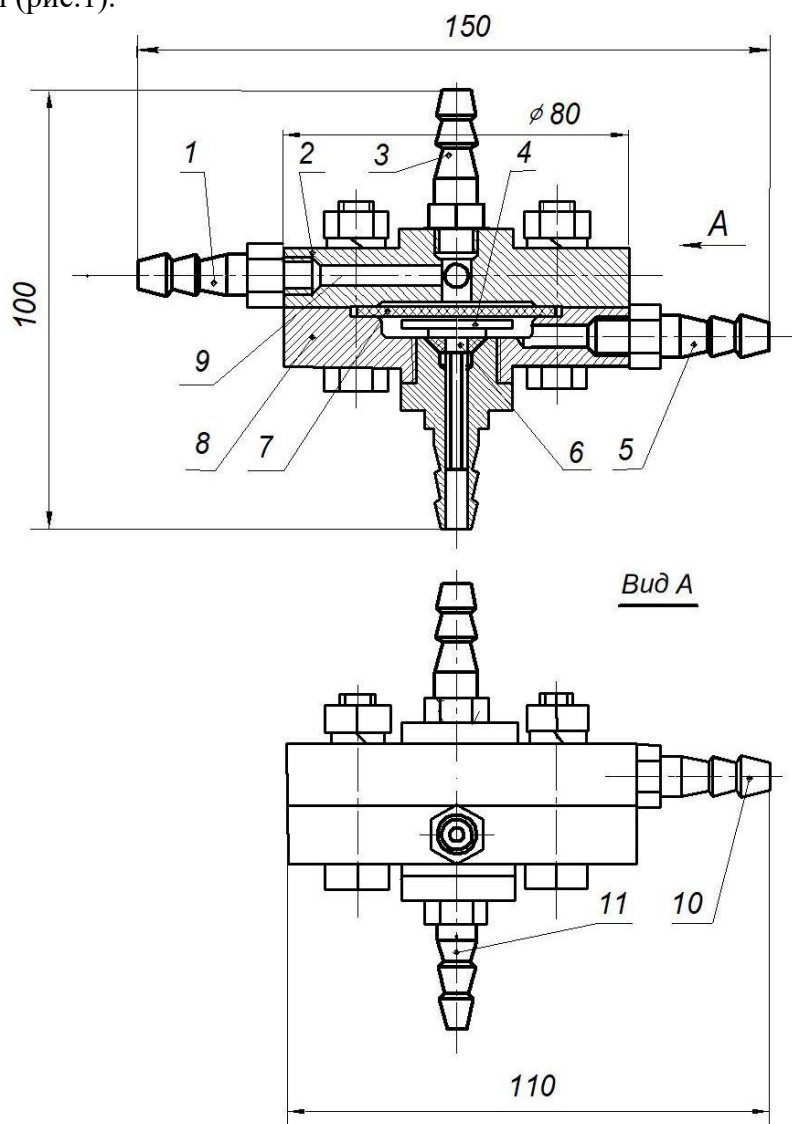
Сухий затвор для воднево-кисневої зварювальної установки:
